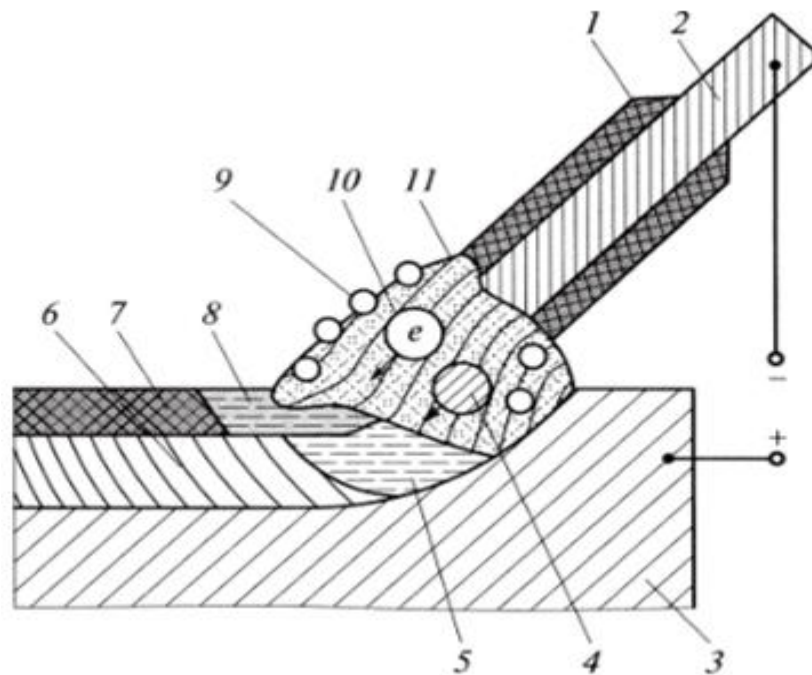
Схема процесу ручного дугового зварювання:
